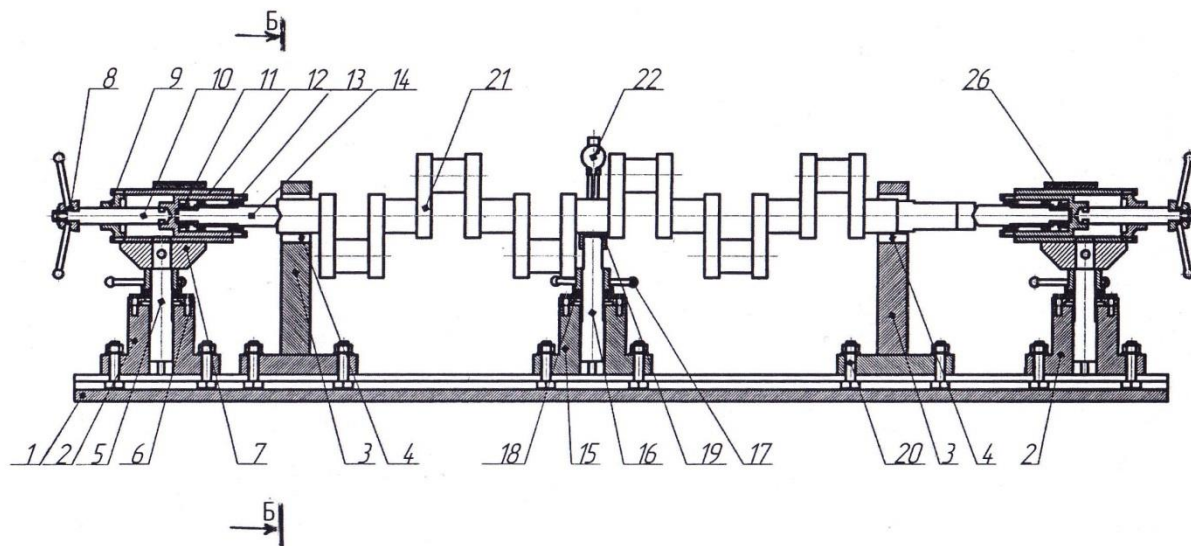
Новое устройство для проверки изгиба коленчатого вала на центрах и выпрямления на гидравлическом прессе
